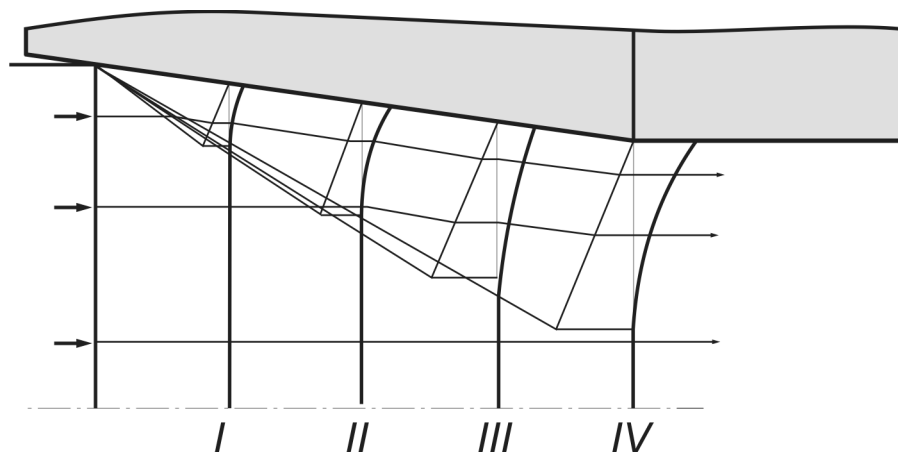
Изменение контура торцевой поверхности при движении заготовки в зоне первичного захвата
